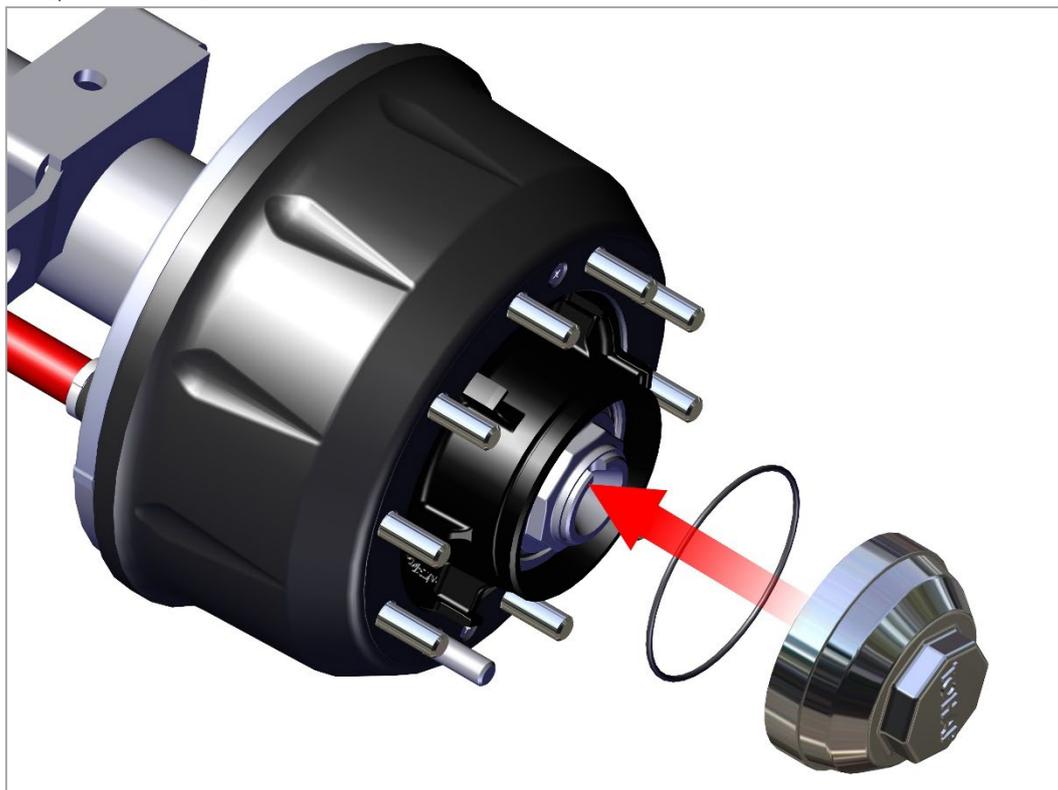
Монтаж крышки ступицы колеса с резиновым уплотнительным кольцом
